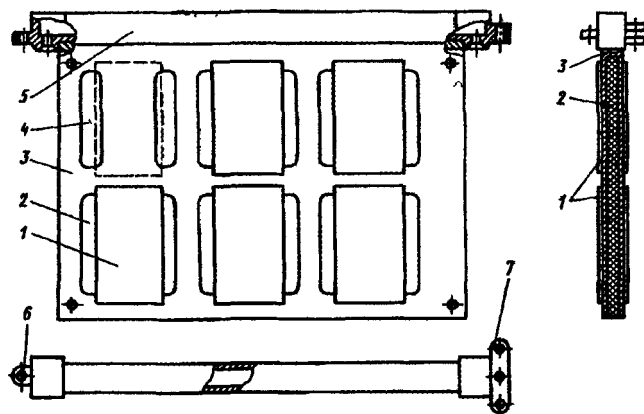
Конструкция двухсторонней ФЯ на металлическом П-образном основании: 7 — микросборка; 2 — многослойная печатная плата; 3 — основание; 4 — окно для выводов; 5 — воздухопровод; 6,7 — шарнирные соединения
